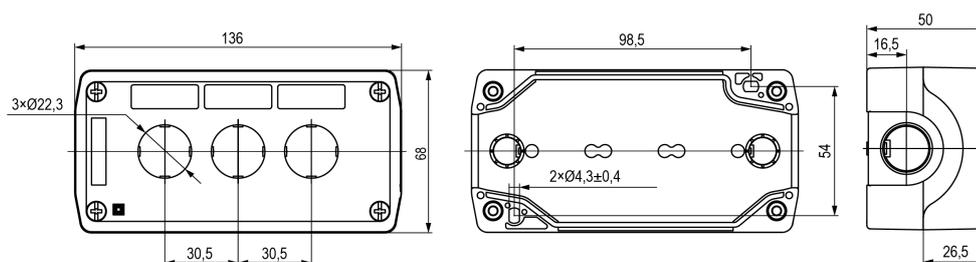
Габаритные и установочные размеры трехместного корпуса
